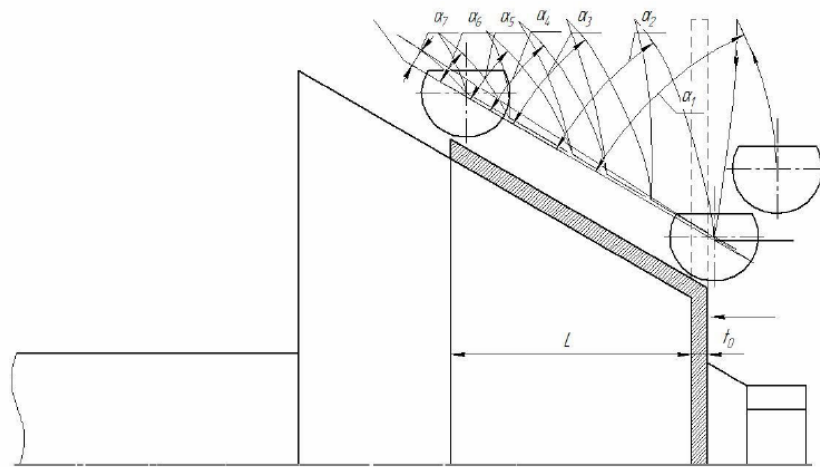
Послідовність ротаційної витяжки заготовки та траєкторії руху інструмента
